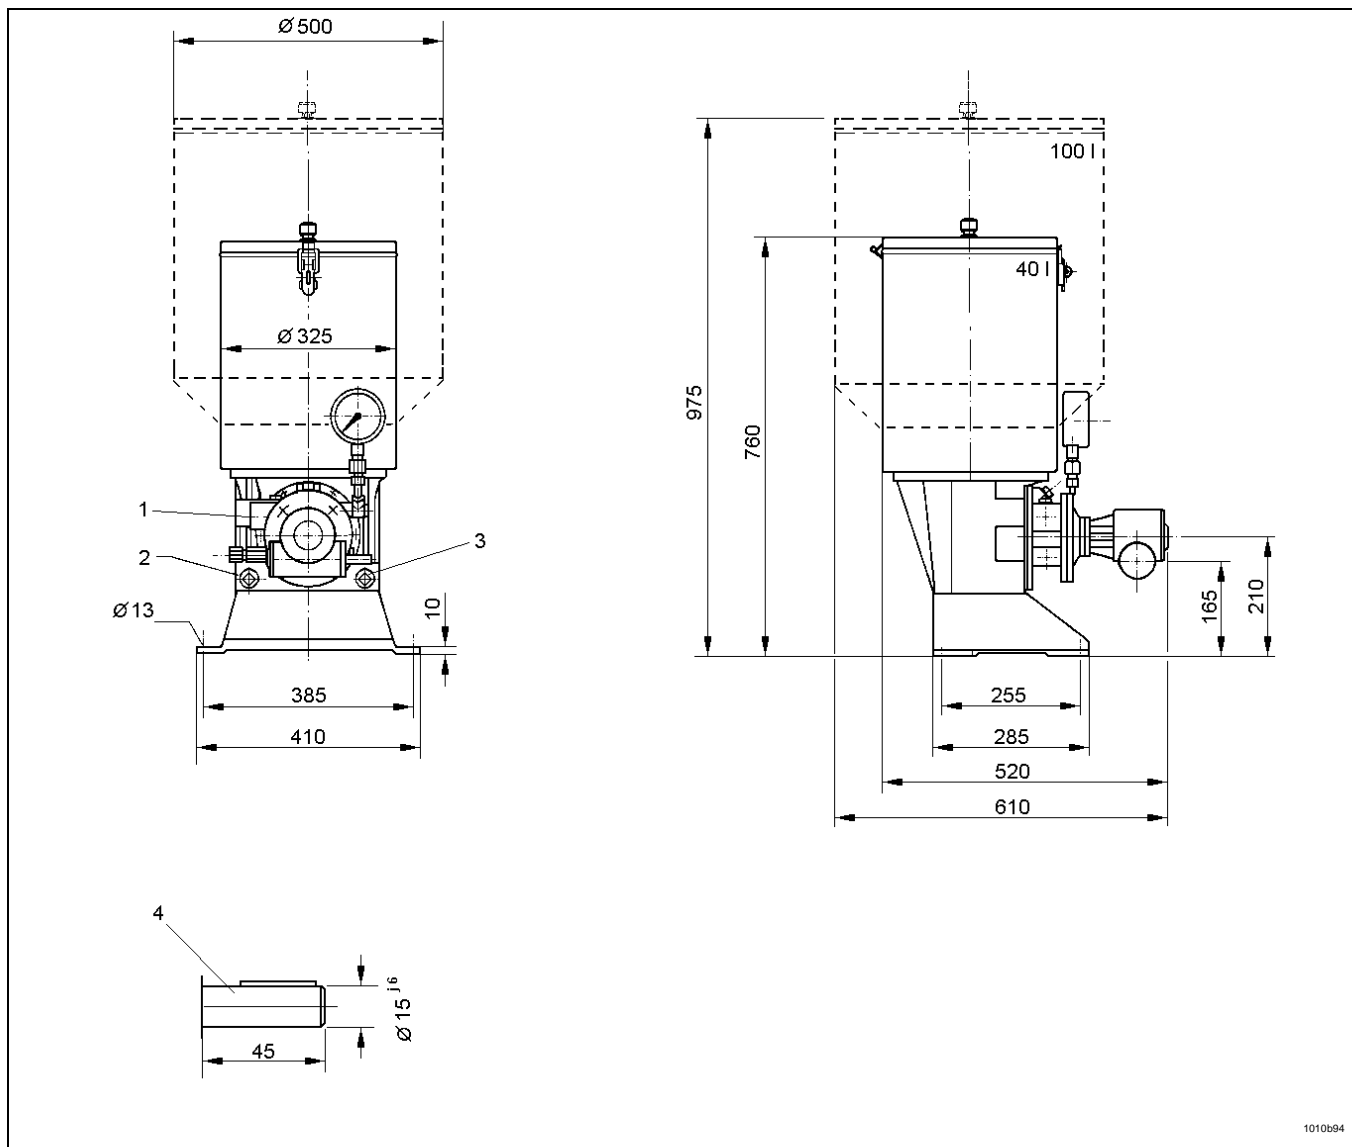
Abmessungen ZPU 08 S F mit angeflanschem Schneckengetriebe
